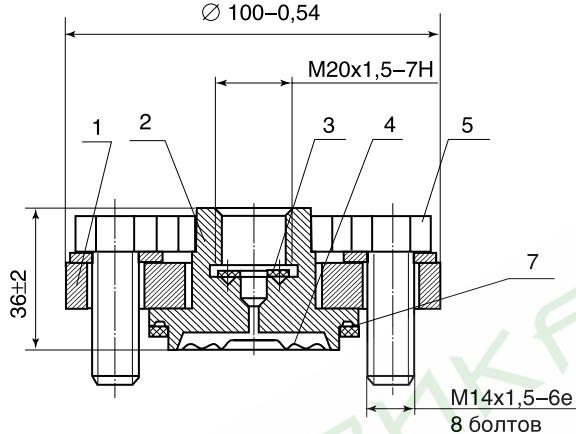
Разделитель мембранный РМ модели 5321. Габаритные и присоединительные размеры
